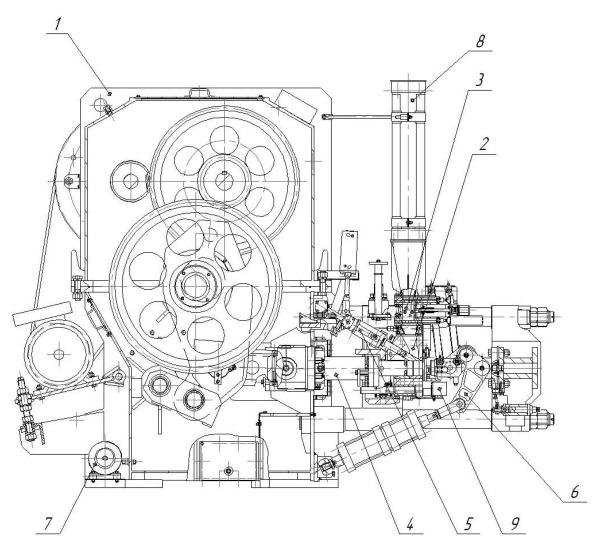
Пресс ШЛ-403Б: 1 — корпус, 2 — камера прессования, 3 — дозатор с предкамерой, 4 — прессующий ползун, 5 — шиберное устройство, 6 — затвор, 7 — система смазки, 8 — загрузочная шахта, 9 — сортировочное устройство.
